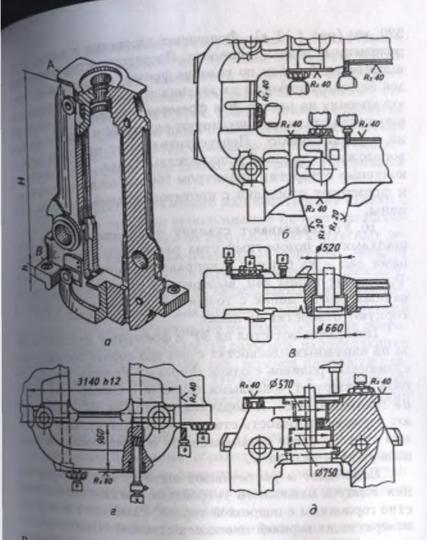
Эскизы основных операций механической обработки станки нарытого тица:
